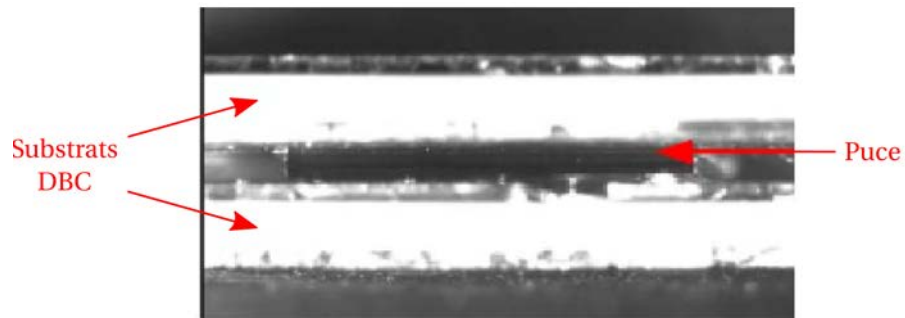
Image d'un assemblage par la technologie DSI [6].
